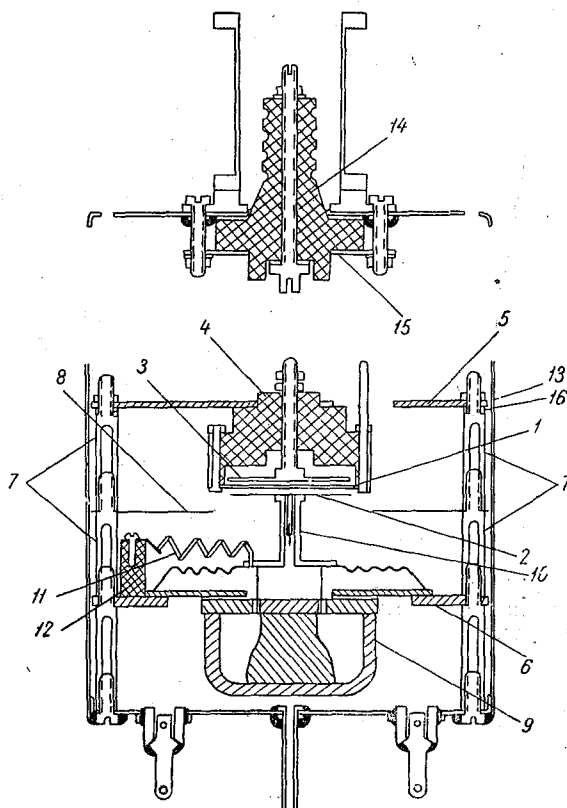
Сечение емкостного динамического преобразователя и крышки герметичного кожуха.
